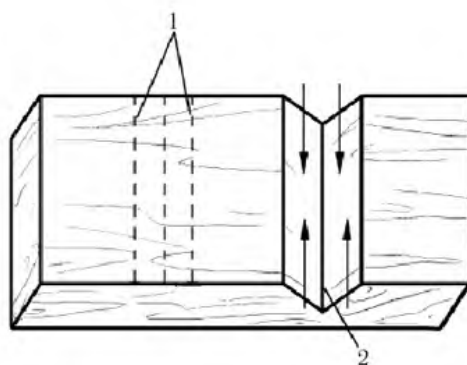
Выполнение прямой двусторонней выемки поперек волокон заготовки (стрелками указано направление движения ножа)
